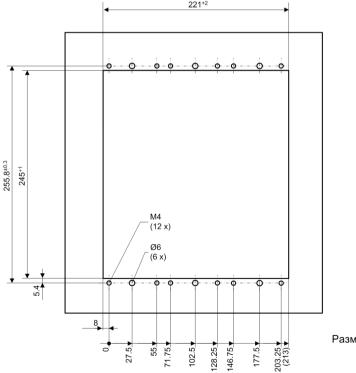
Ширина вырезов и схема сверления отверстий – устройство 1/1, первый ряд устройств
